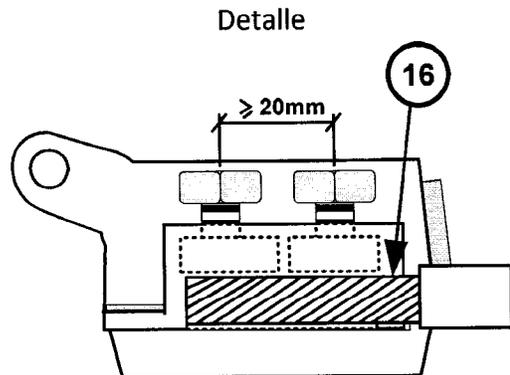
c. Diseño de la bornera con doble tornillo, una vez montado.
